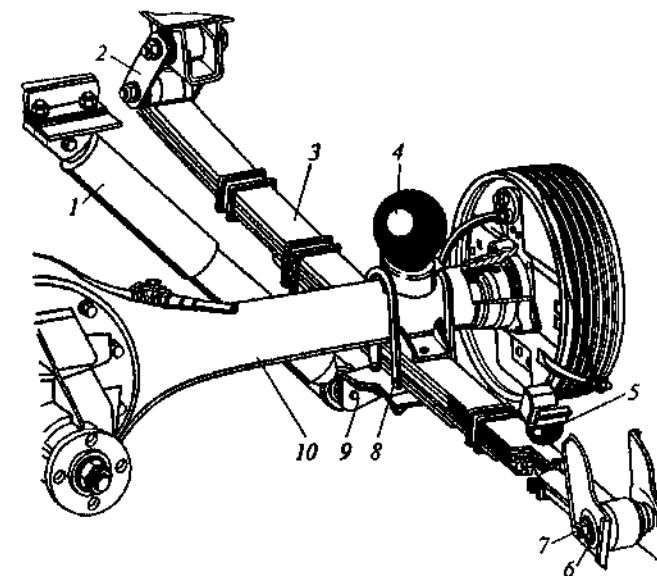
Задняя подвеска легкового автомобиля малого класса: 1 — амортизатор; 2 — серьга; 3 — рессора; 4 и 5 — буфера; 6 — втулка; 7 — палец; 8 — стремянка; 9 — накладка; 10 — балка
